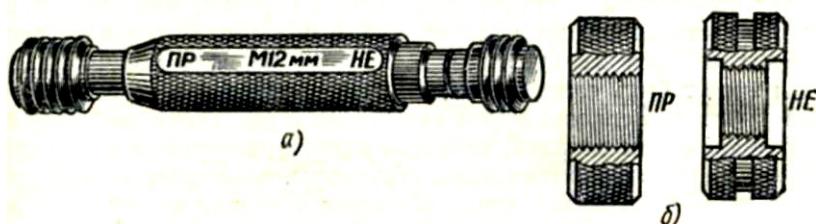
Резьбовые калибры: а – предельная резьбовая пробка, б – нерегулируемые резьбовые кольца
